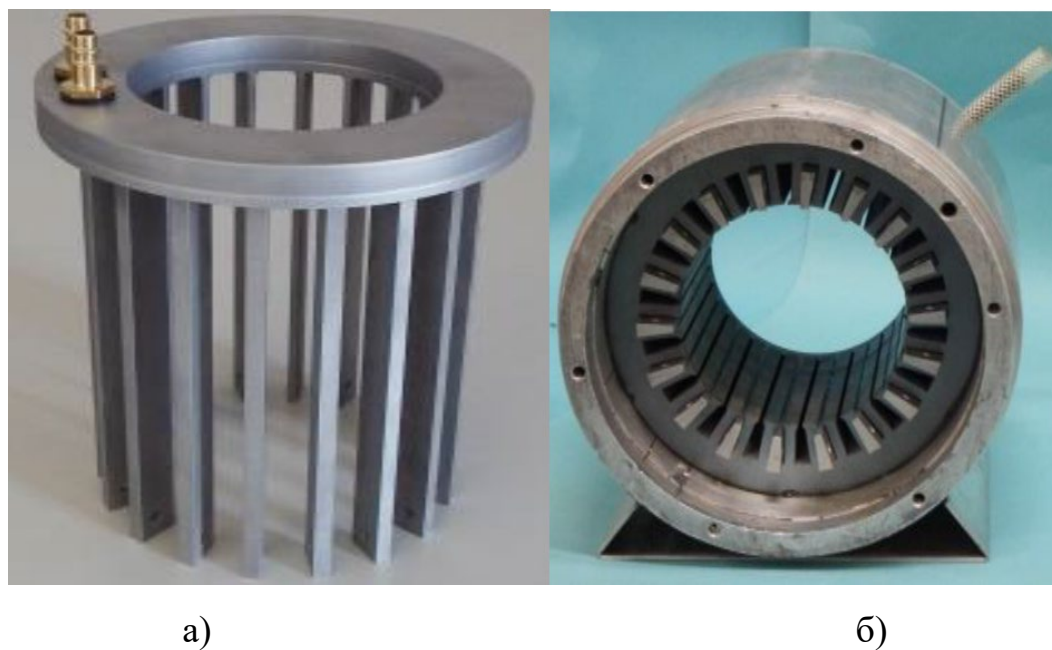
Экспериментальный образец статора электродвигателя ISCAD
